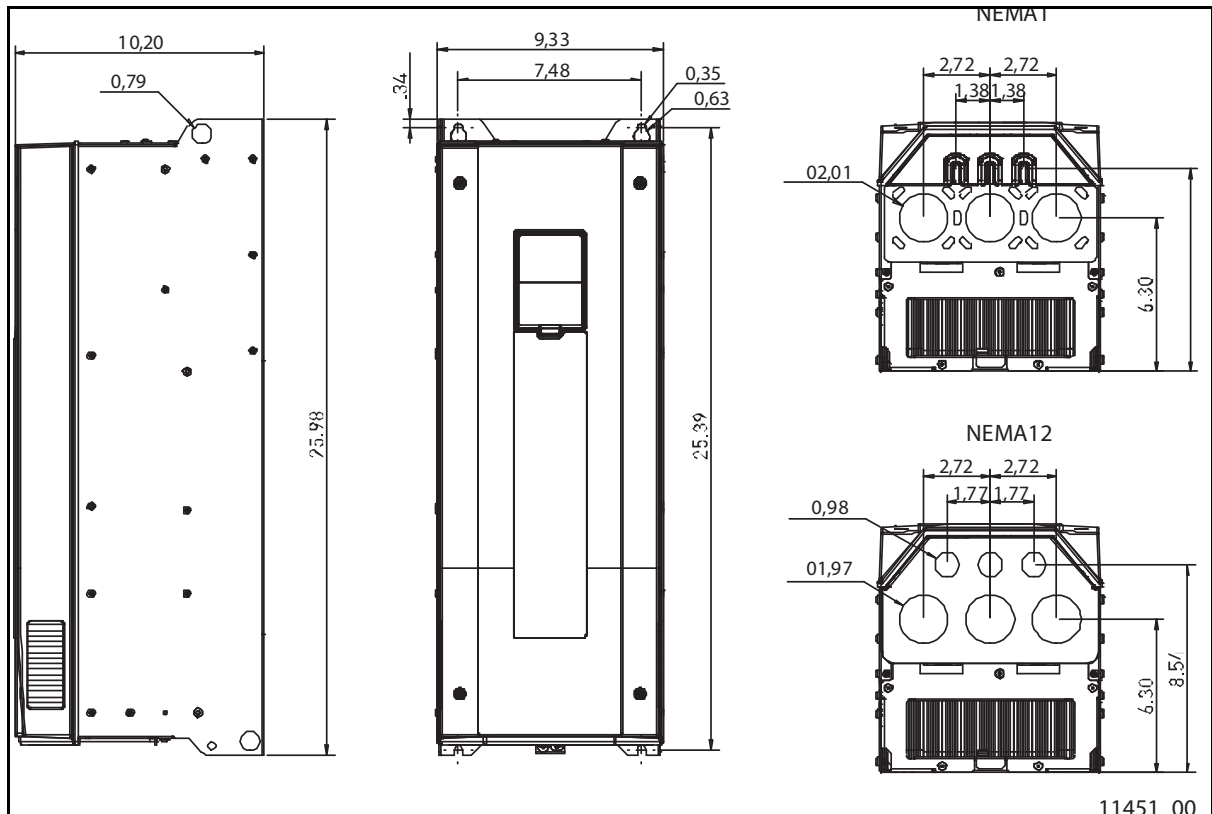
Dimensions de l'appareil SmartVFD HVAC, châssis MR7, montage mural
